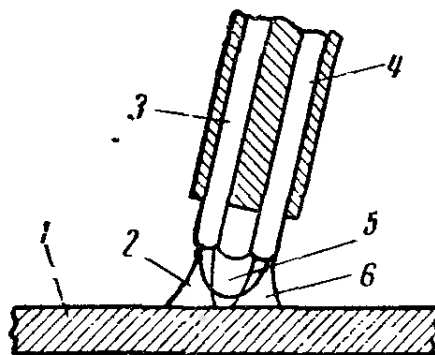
Схема горения трех сварочных дуг при ручной сварке трехфазной дугой
